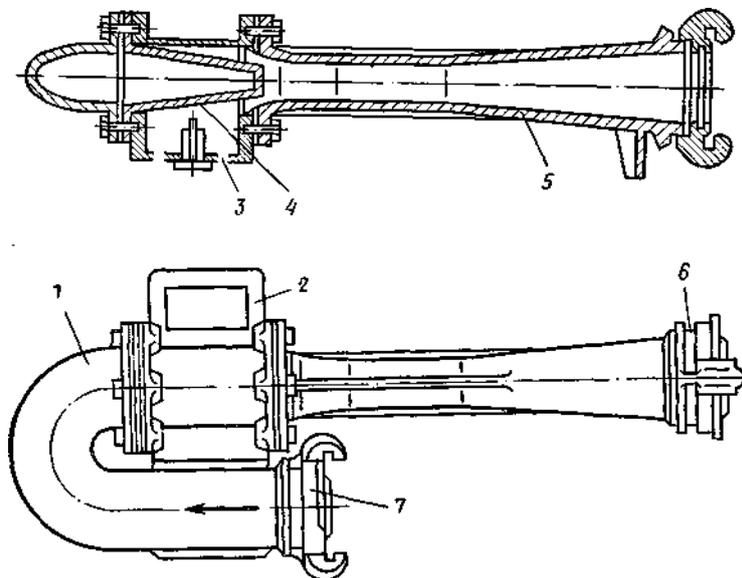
Гидроэлеватор Г-600А: 1 – колено; 2 – камера; 3 – решетка; 4 – сопло; 5 – диффузор; 6 – головка соединительная ГМ-80; 7 – головка соединительная ГМ-70
